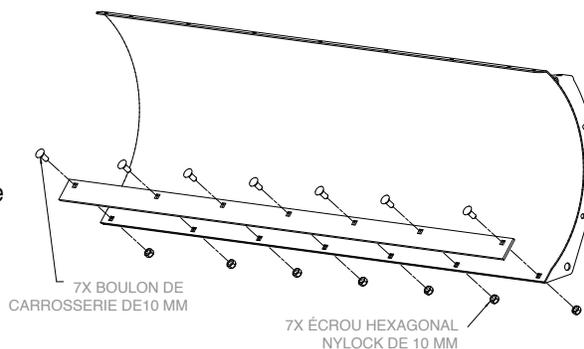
Assemblage de la barre d'usure au chasse-neige
